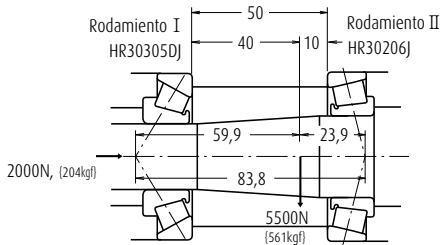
Cargas sobre rodamientos de rodillos cónicos
